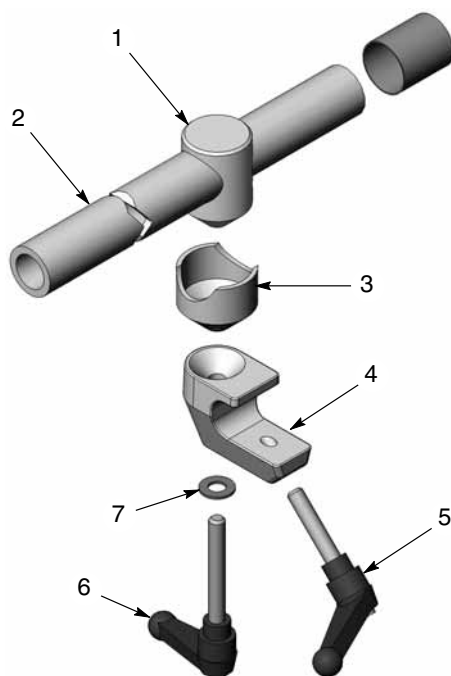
Pistoolbevestiging met extrusieprofiel voor buisbevestigd pistool
